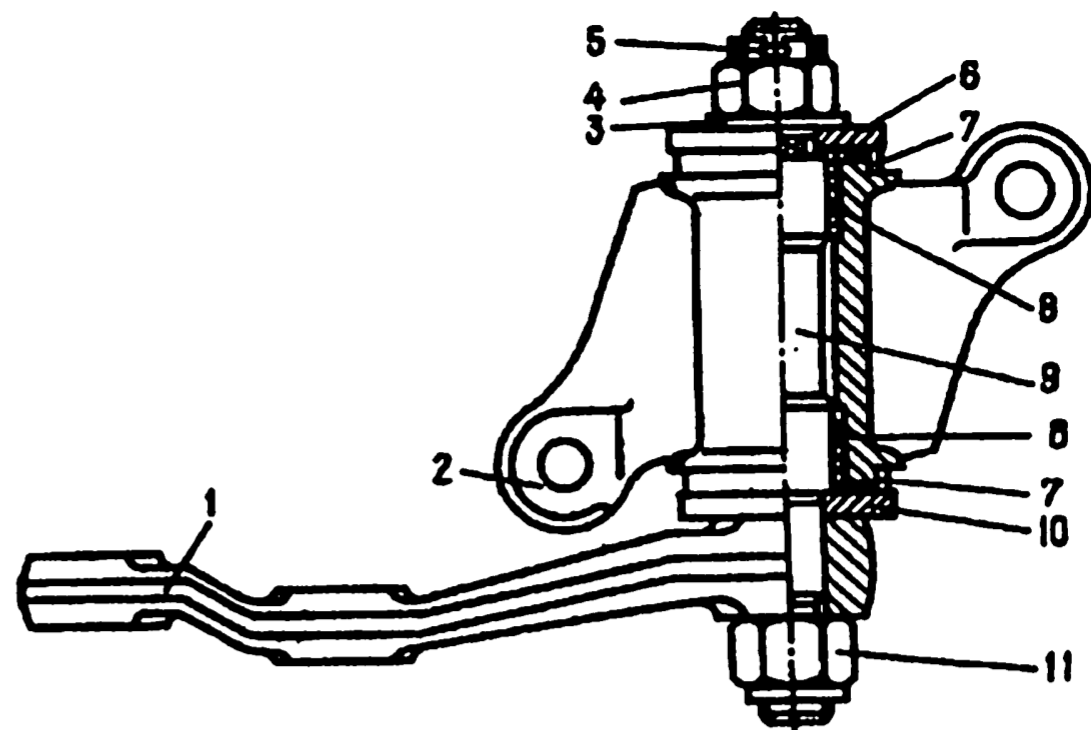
Разрез кронштейна маятникового рычага: 1 - маятниковый рычаг; 2 - корпус кронштейна; 3 - шайба; 4 - регулировочная гайка; 5 - шплинт; 6 - верхняя шайба; 7 - уплотнитель; 8 - втулка; 9 - ось рычага; 10 - нижняя шайба; 11 - самоконтрящаяся гайка
